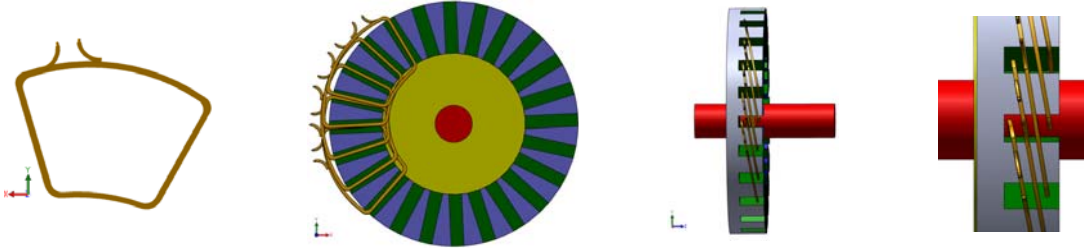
Bobinagem no motor em disco com passo entre bobinas de 4 cavas (bobina à esquerda).
